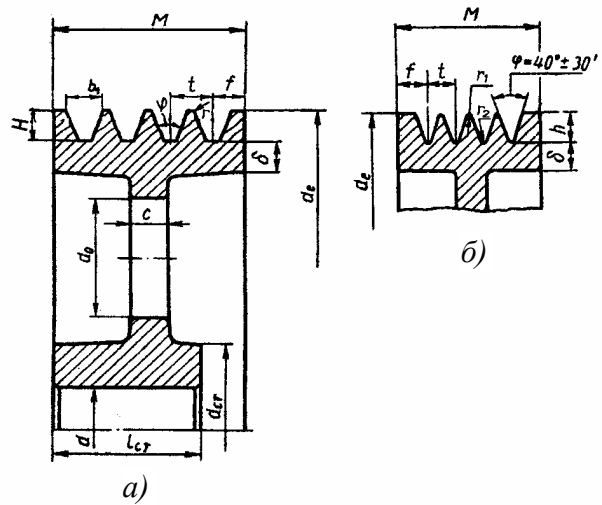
Конструкции шкивов для клиновых и поликлиновых ремней
